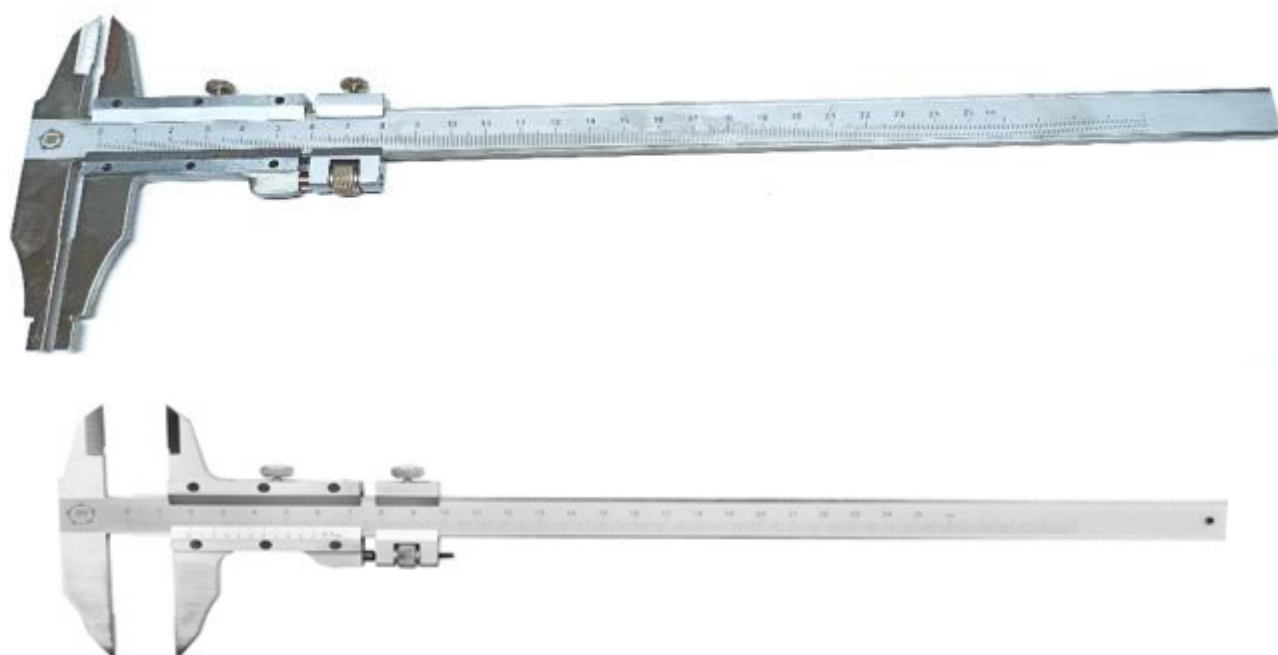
Общий вид штангенциркулей ШЦ типа II
